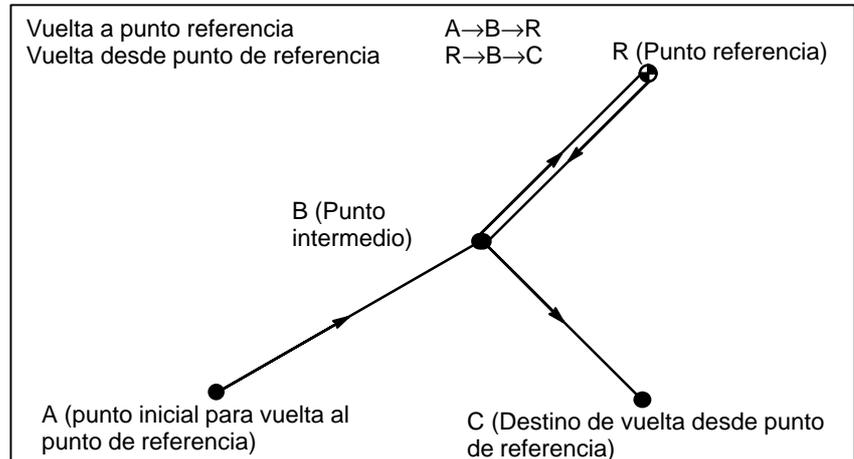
(b) Vuelta a punto de referencia y vuelta desde punto de referencia
